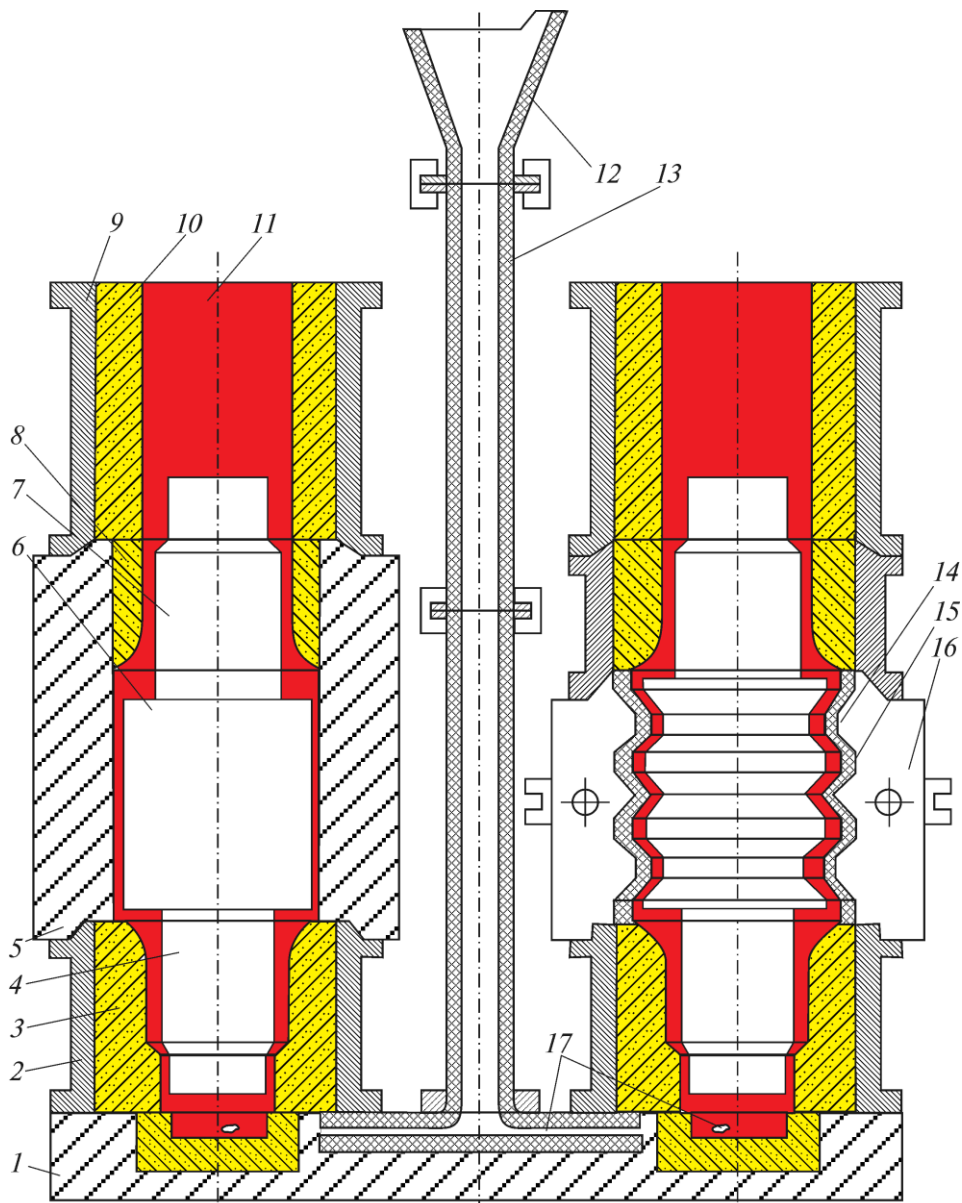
Схема форми для лиття валків з гладкою бочкою і з литими калібрами (тонкими лініями позначені чистові розміри валків) [3]: 1-двомісний піддон; 2-форма нижньої шийки; 3-формувальна суміш; 4-нижня шийка прокатного валка; 5-кокіль; 6-бочка прокатного валка; 7-верхня шийка прокатного валка; 8- «закладення» - формувальна суміш в кокілі; 9-форма надливу; 10-формувальна суміш надливу; 11-надлив; 12-лійка; 13-стояк; 14-виступ калібру кокілю; 15-западина калібру кокілю; 16-кокіль з литими калібрами і вертикальним роз'ємом; 17-тангенціальний живильник
